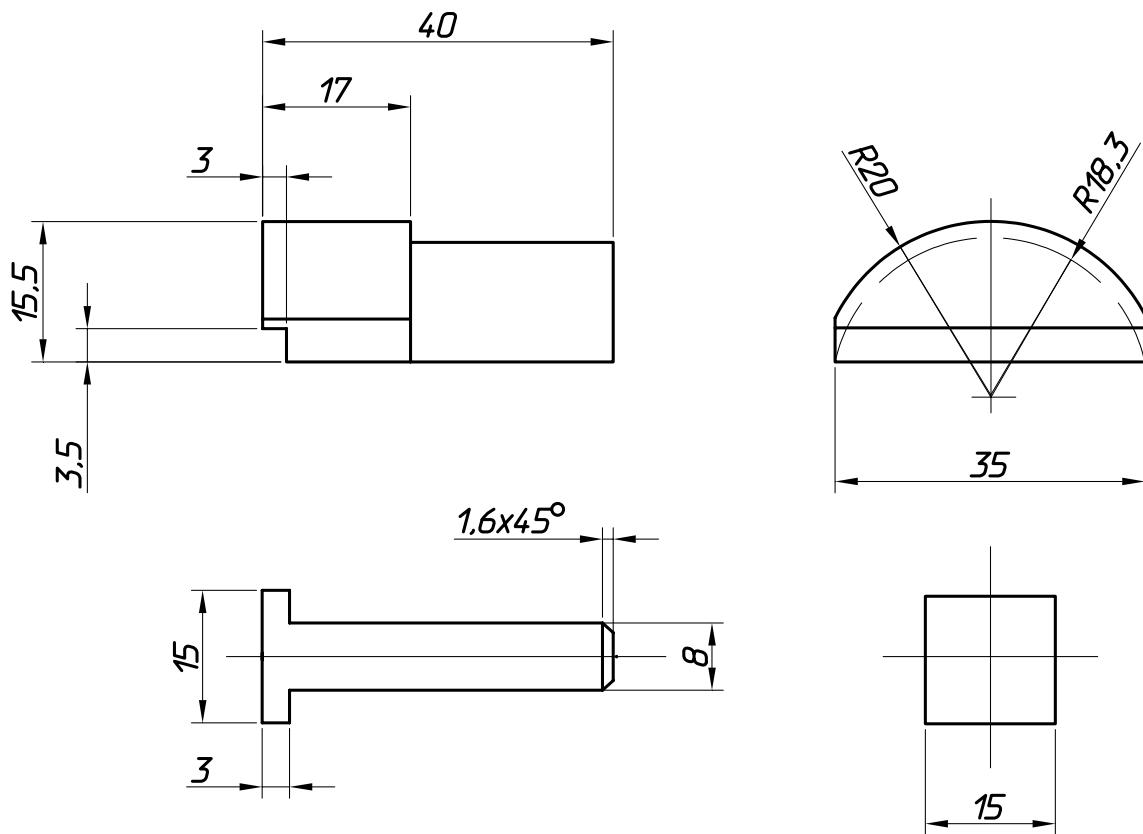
Приспособление для выпрессовки распорной втулки
